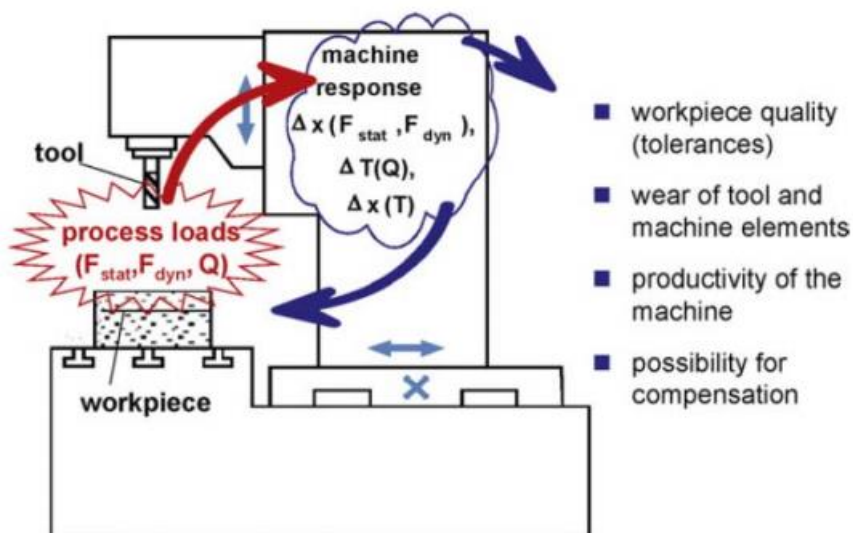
Wechselwirkungen zwischen Prozess und Werkzeugmaschine¹⁸
